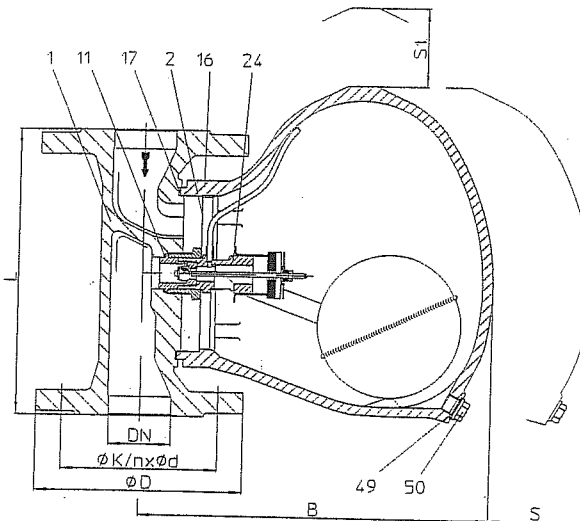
1 mit Flanschen - vertikale Einbaulage
